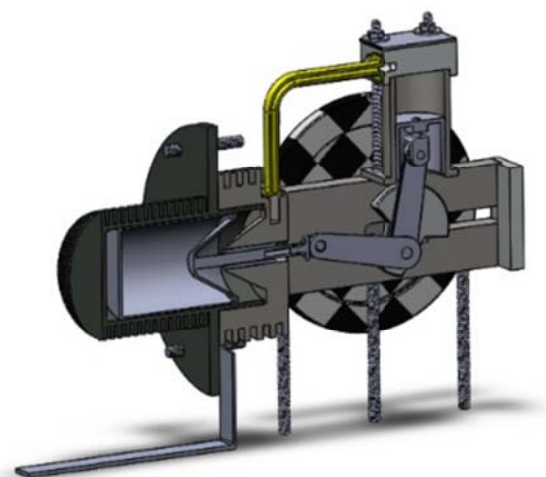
3D модель двигателя Стирлинга в разрезе
